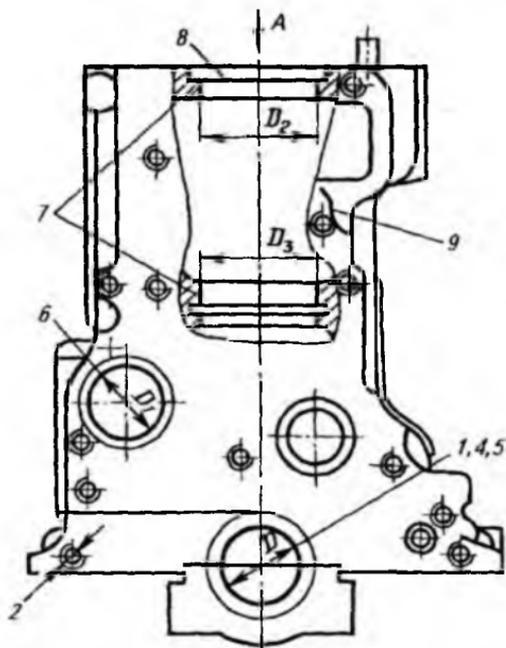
Схема блока цилиндров двигателя Д-240:
